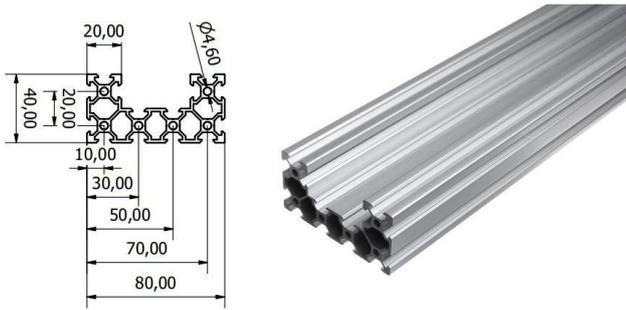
Perfil Alumínio Estrutural C-Beam 80x40mm
